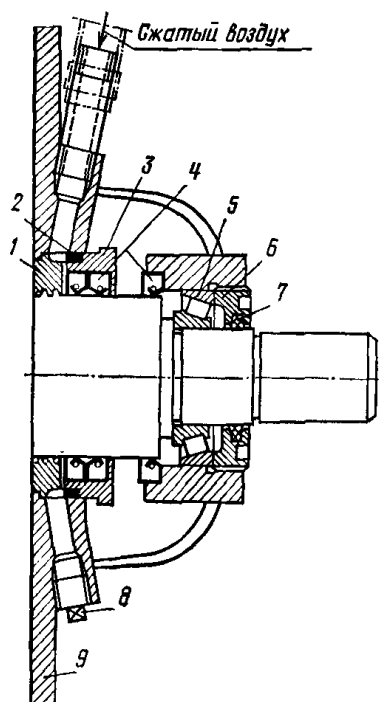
Шлюзовой питатель РЗ-БШП
